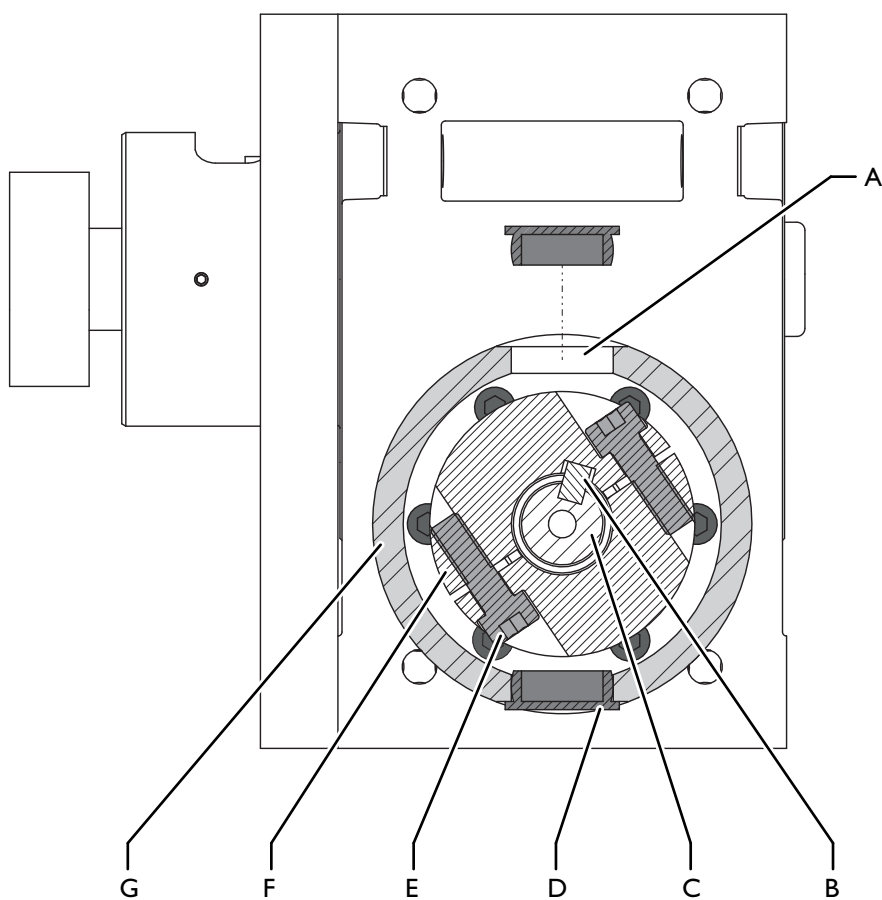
Выставить ведущий вал к редукторному фланцу
